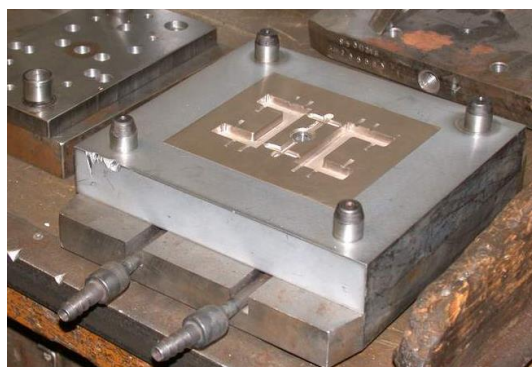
Вставка для ТПА и отливки из ABS-пластика.
